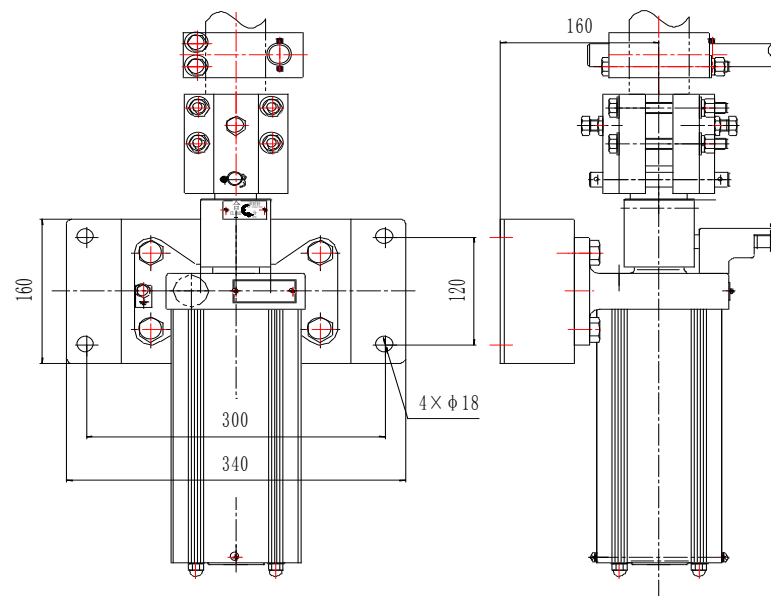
Внешний вид и габаритно-установочные размеры ручного привода заземляющих ножей РГП
